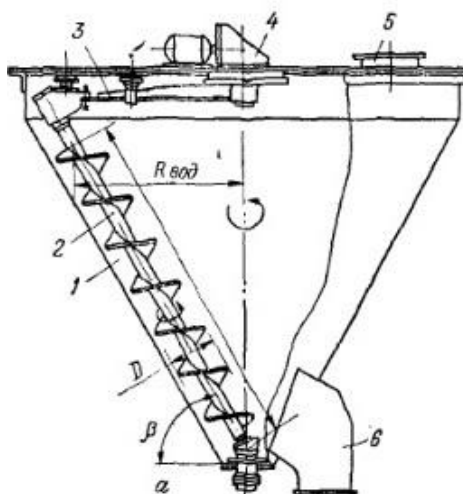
Планетарный шнековый смеситель непрерывного действия:
